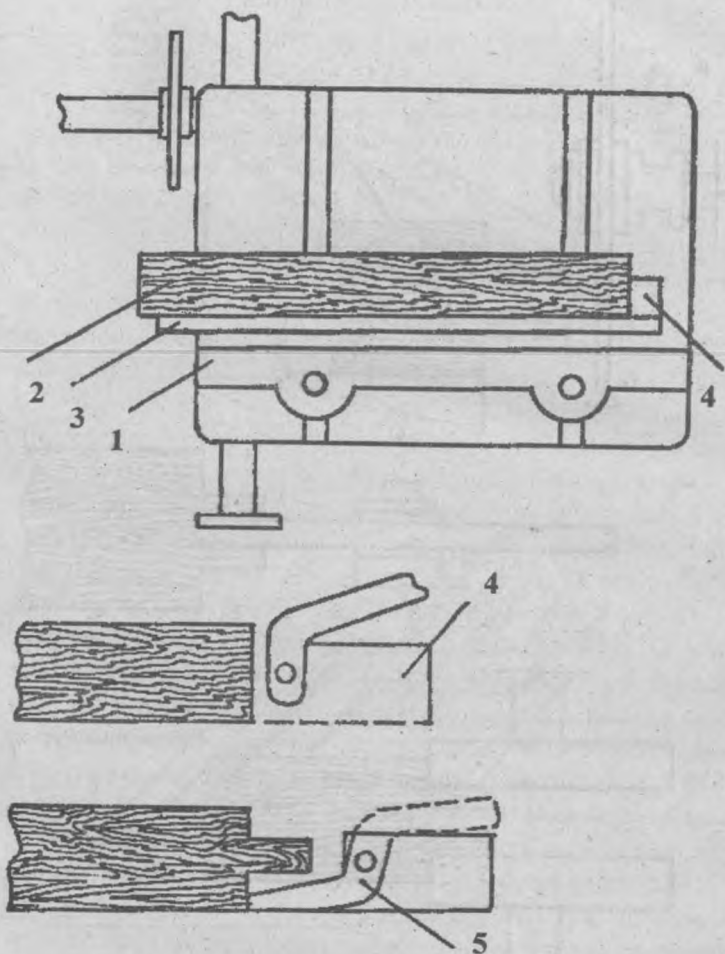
Установка торцового упора на каретке шипорезного станка:
